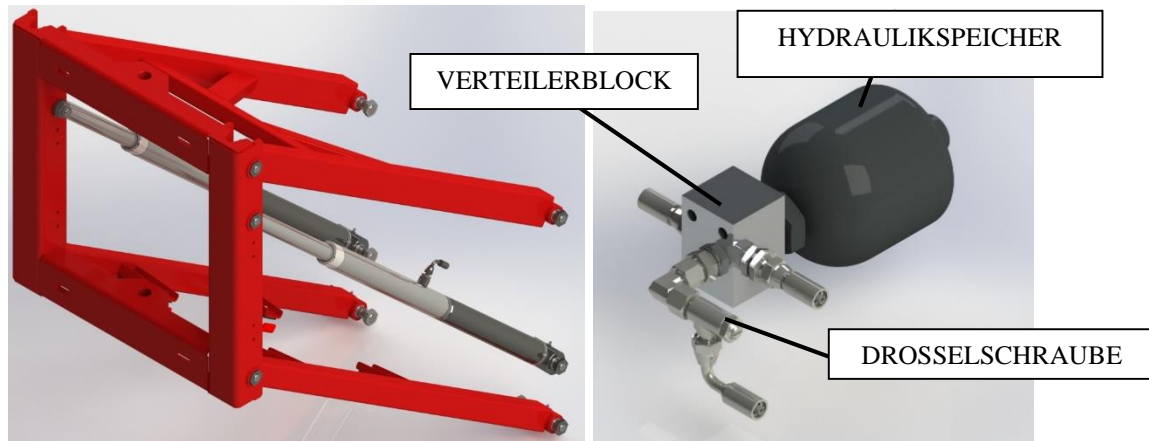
HYDRAULISCHES TRAPEZ-HEBEWERK UND HYDRAULIKSPEICHER
